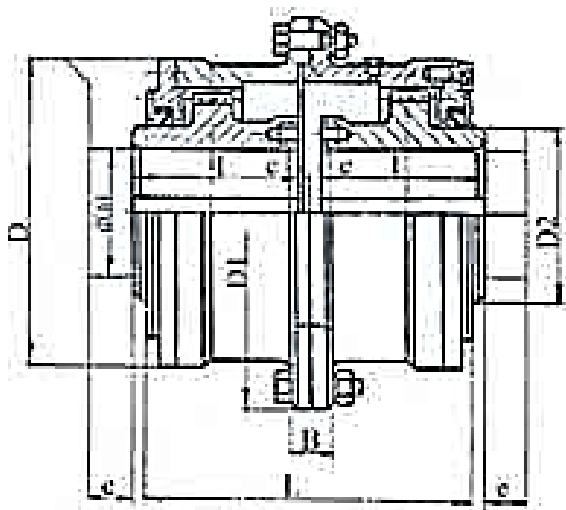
Эскиз зубчатой муфты конструкции ОАО «ЭЗТМ»:
